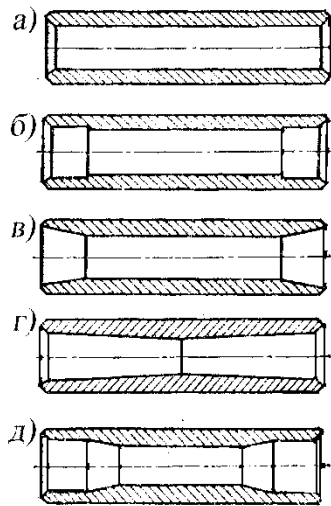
Конструктивные формы поршневого пальца: *a, б* – цилиндрические; *в-д* –приближающиеся к балке равного сопротивления
